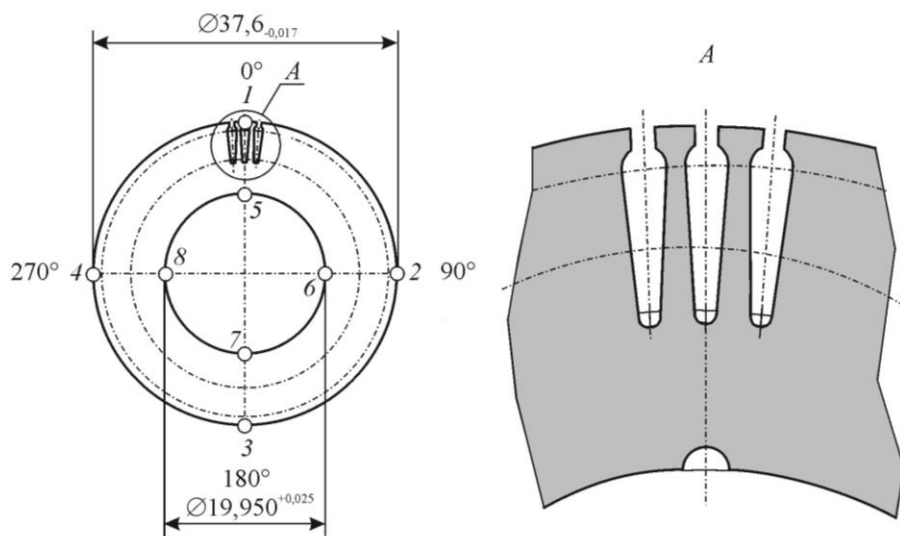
Схема виміру висоти задирки пластини ротора:
